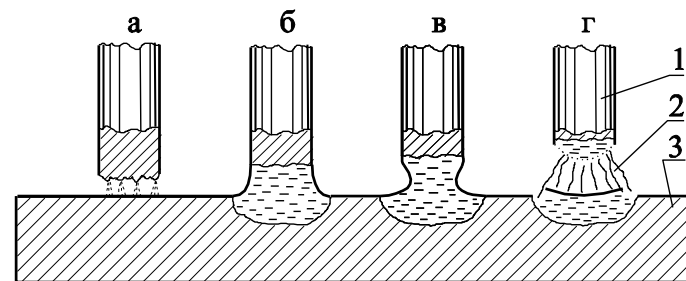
Возникновение сварочной дуги: а - короткое замыкание; б - образование прослойки жидкого металла; в - образование шейки; г - возникновение дуги. 1 - электрод; 2 - дуга; 3 - свариваемый металл.
